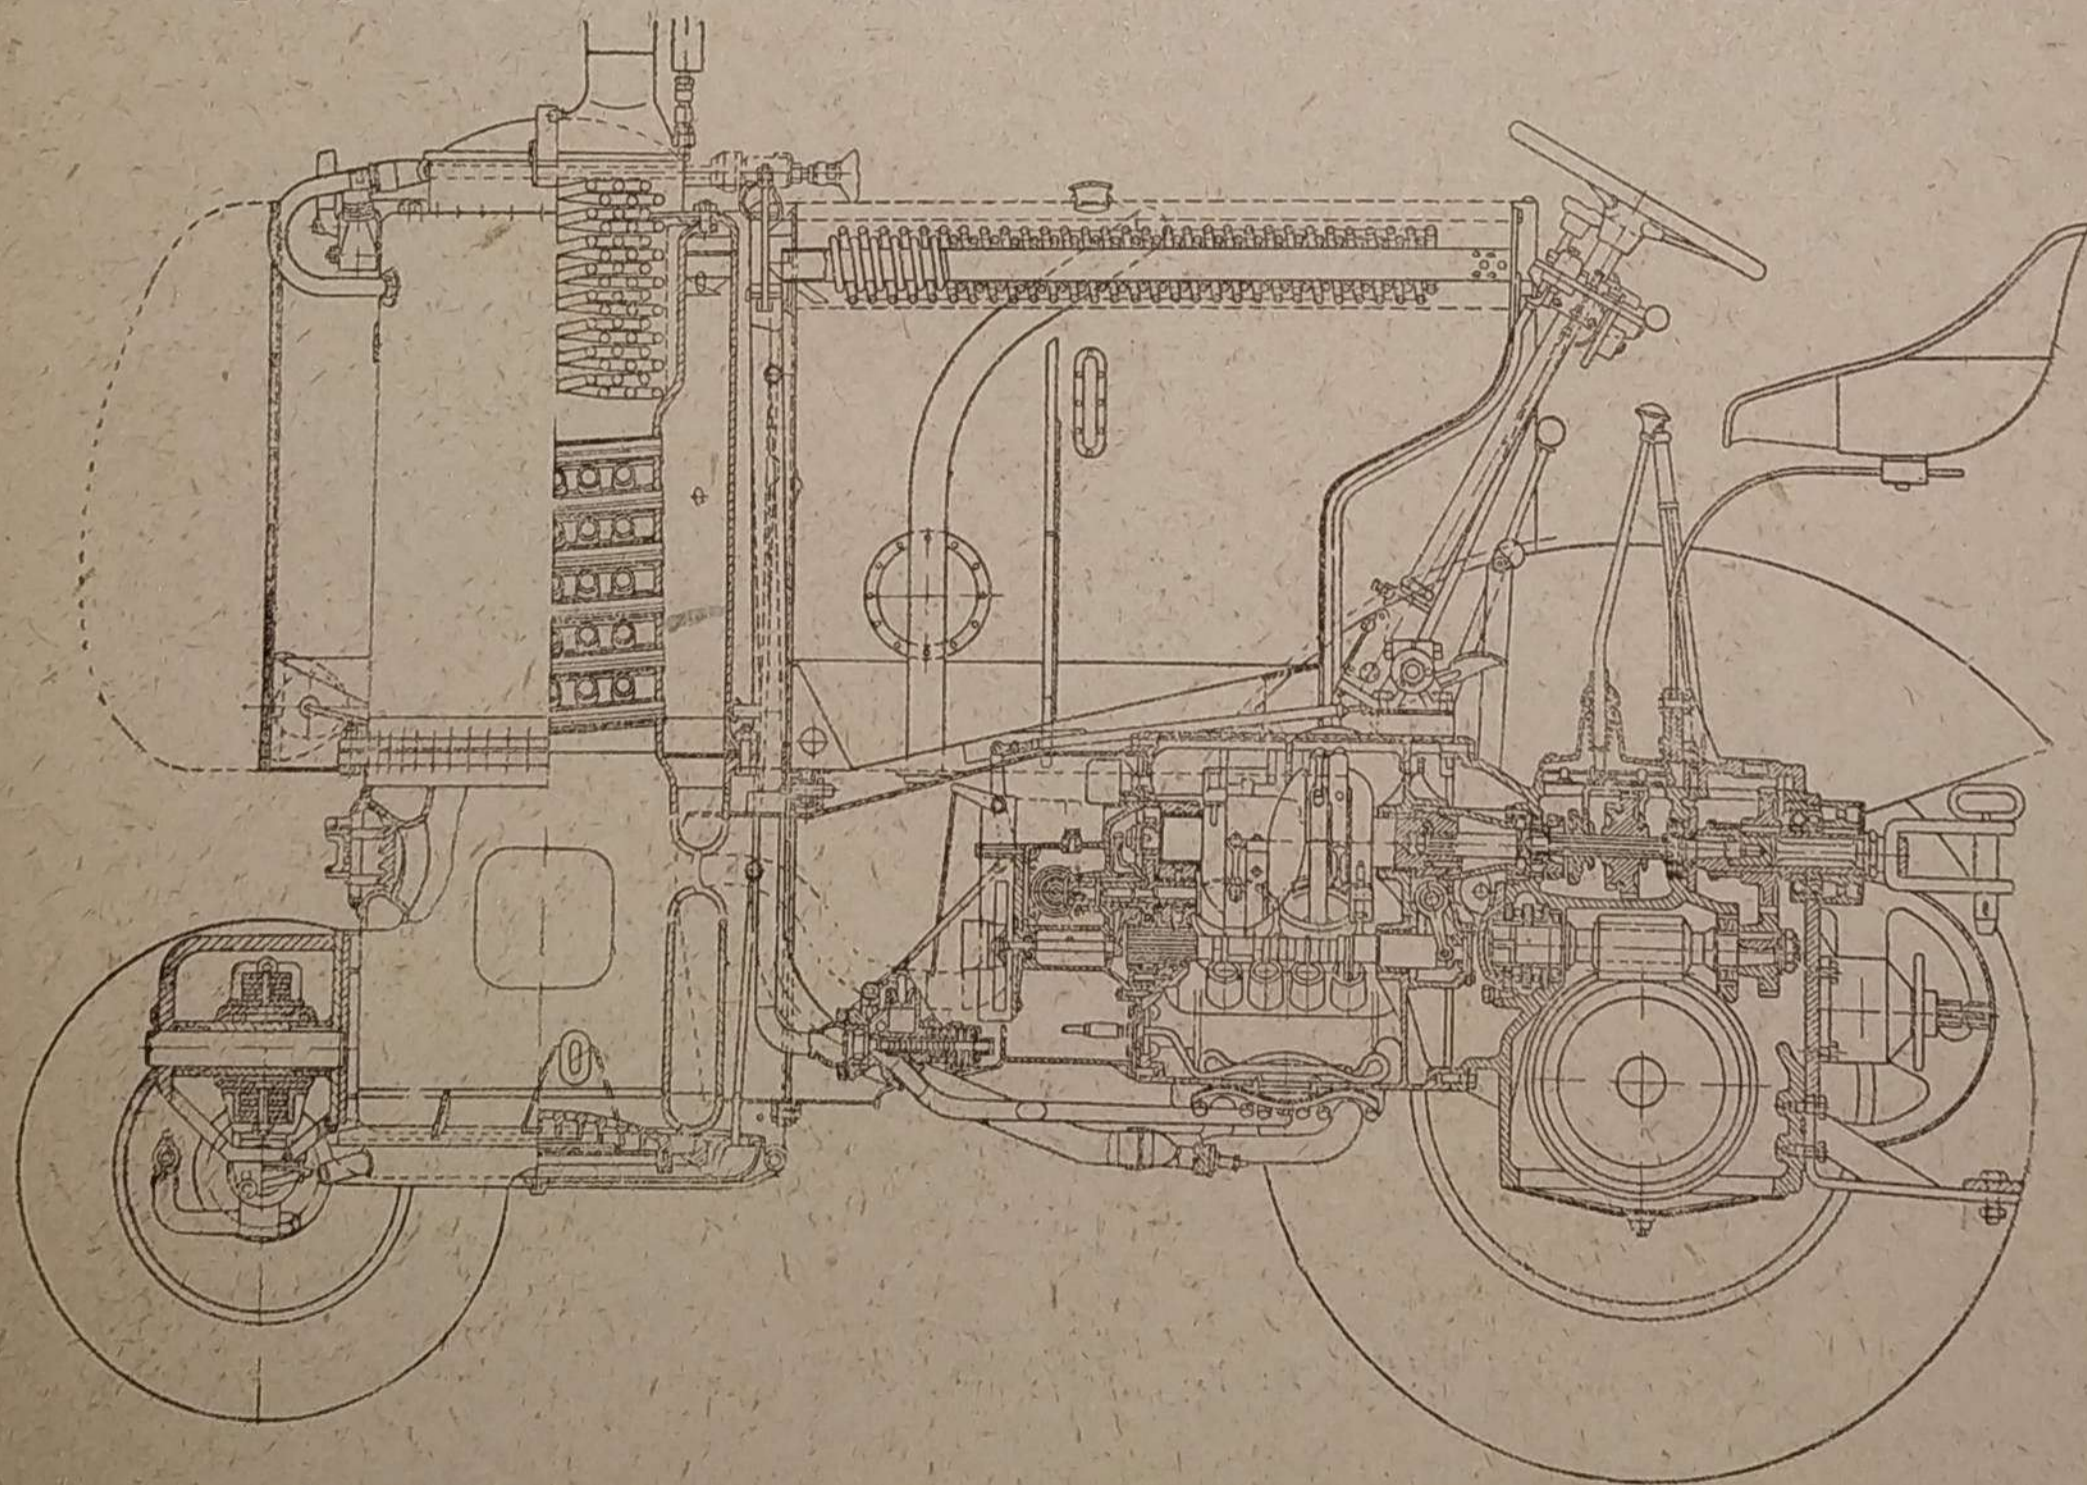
Размещение агрегатов паросиловой установки на шасси.
